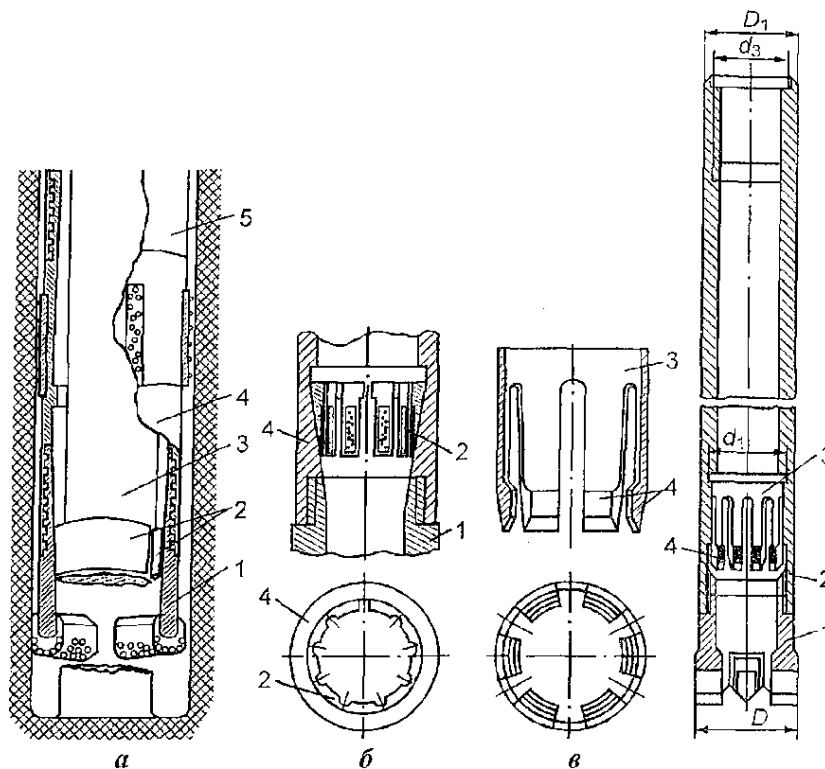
Схемы керноз ахватывающих устройств: а, б- кольцевой формы: 1- коронка; 2- керноз ахватывающий элемент; 3- керн; 4 - корпус кернорвателя; 5 - колонковая труба; в - цангового типа: 1- корпус коронки; 2 - коническая проточка; 3 - корпус кернорвателя; 4 - керноз ахватывающие элементы
